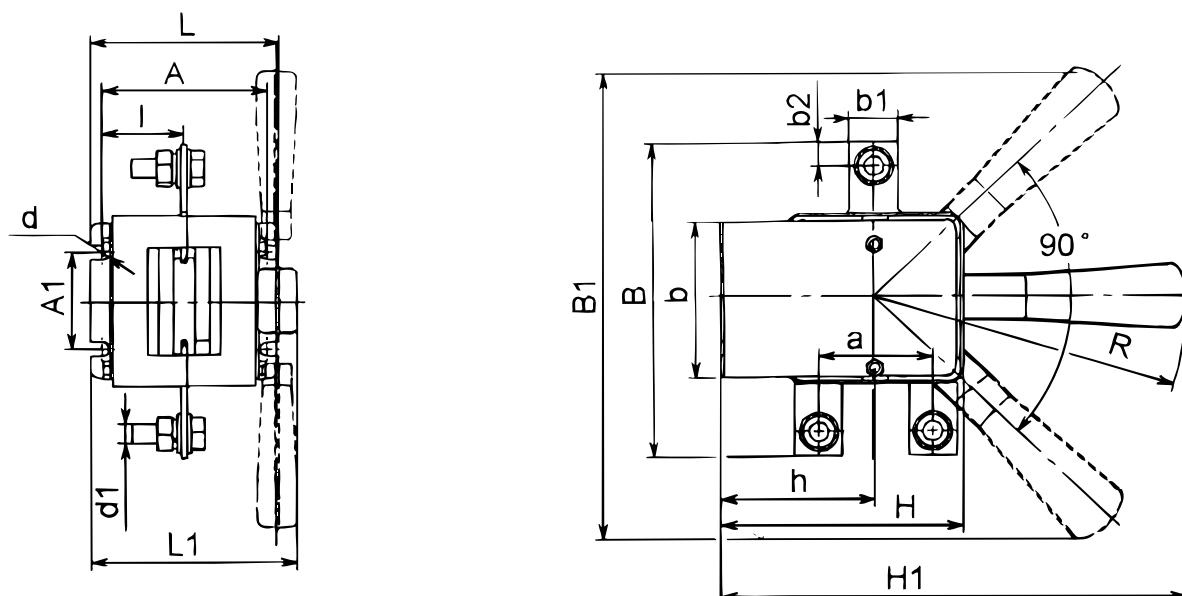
Выключатель-разъединитель однополюсный на два направления с боковой рукояткой
